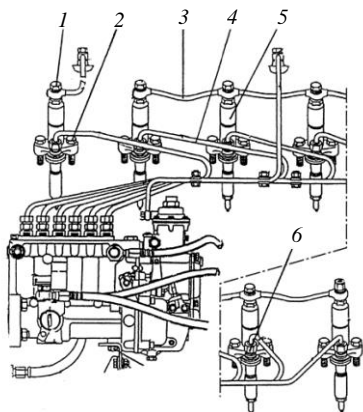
Демонтаж форсунок: 1 – болт штуцера слива; 2 – болт крепления форсунки; 3 – сливной трубопровод; 4 – трубка высокого давления; 5 – форсунка; 6 – накидная гайка штуцера ТНВД
